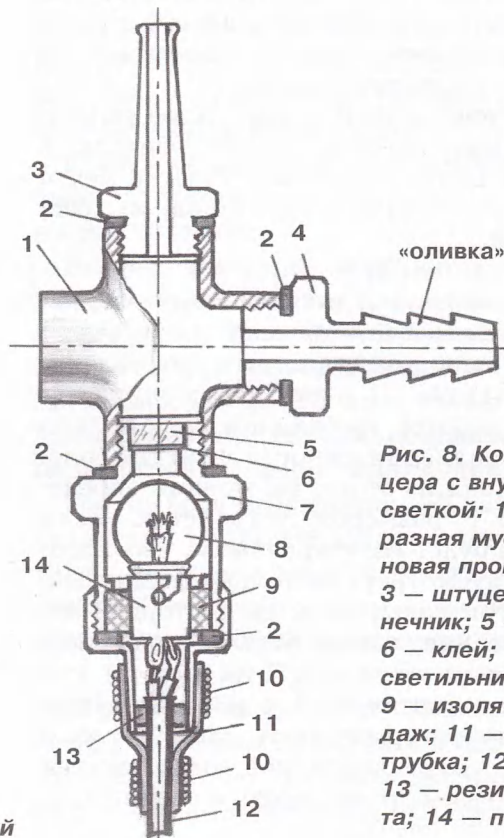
Конструкция штуцера с внутренней подсветкой: 1 — крестообразная муфта; 2 — резиновая прокладка; 3 — штуцер; 4 — наконечник; 5 — стекло; 6 — клей; 7 — корпус светильника; 8 — лампа; 9 — изолятор; 10 — бандаж; 11 — резиновая трубка; 12 — кабель; 13 — резиновая манжета; 14 — патрон.
